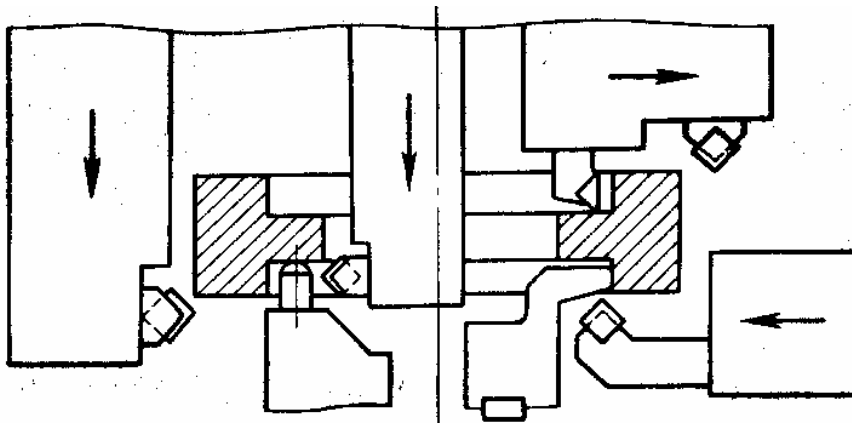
Схема налагодження двошпindelного вертикального напівавтомата для обробки заготовки зубчатого колеса
